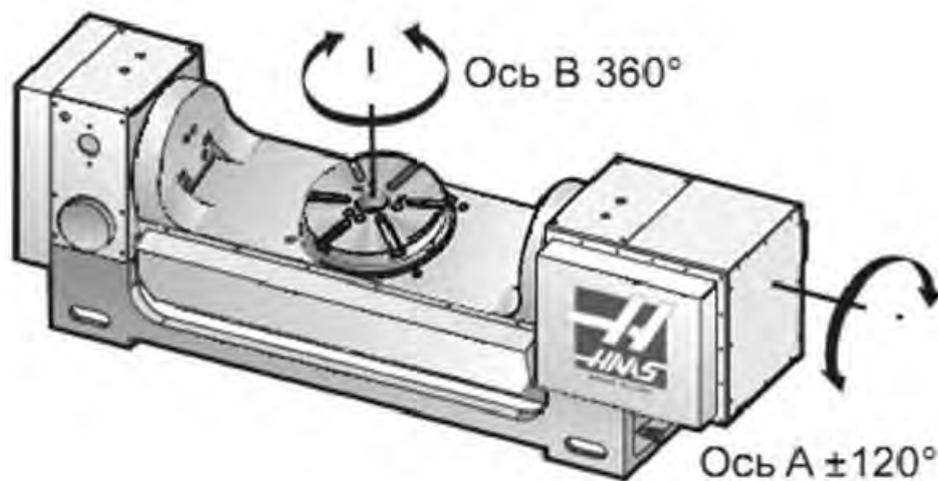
Наклонно-поворотный стол для делительного движения сателлита на фрезерном станке с ЧПУ
